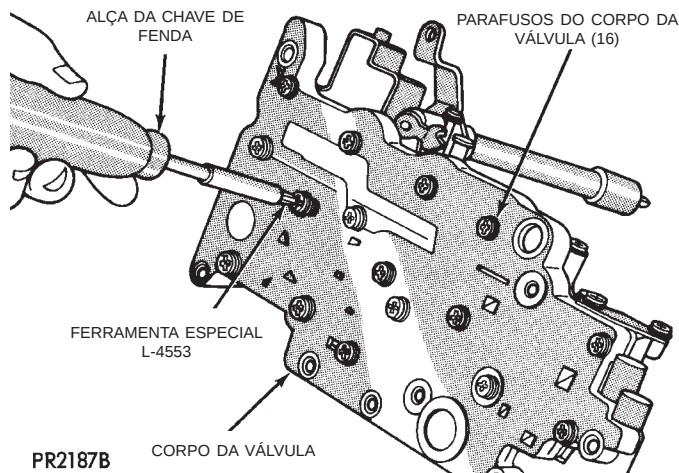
Remoção ou Instalação dos Parafusos do Corpo da Válvula
